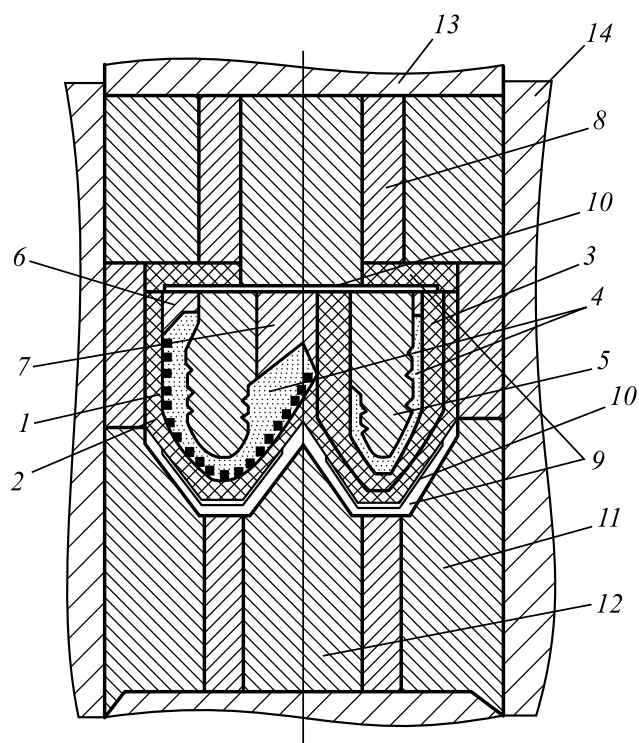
Схема сборки КВД для горячего прессования алмазных долот:
